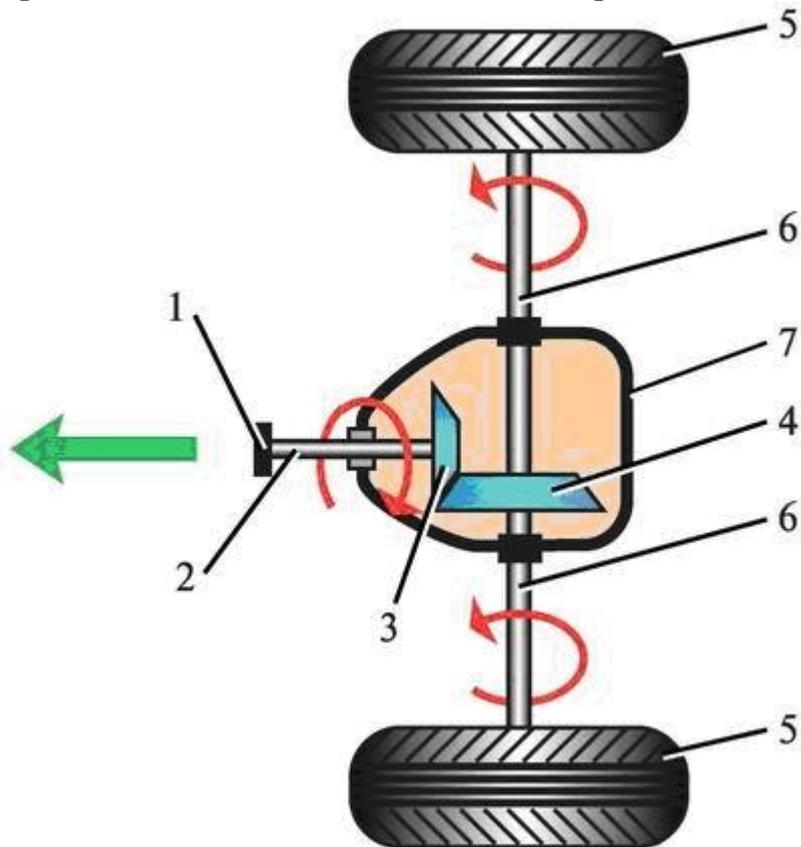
Схема работы главной передачи: 1 - фланец; 2 - вал ведущей шестерни; 3 - ведущая шестерня; 4 - ведомая шестерня; 5 - ведущие (задние) колеса; 6 - полуоси; 7 - картер главной передачи
